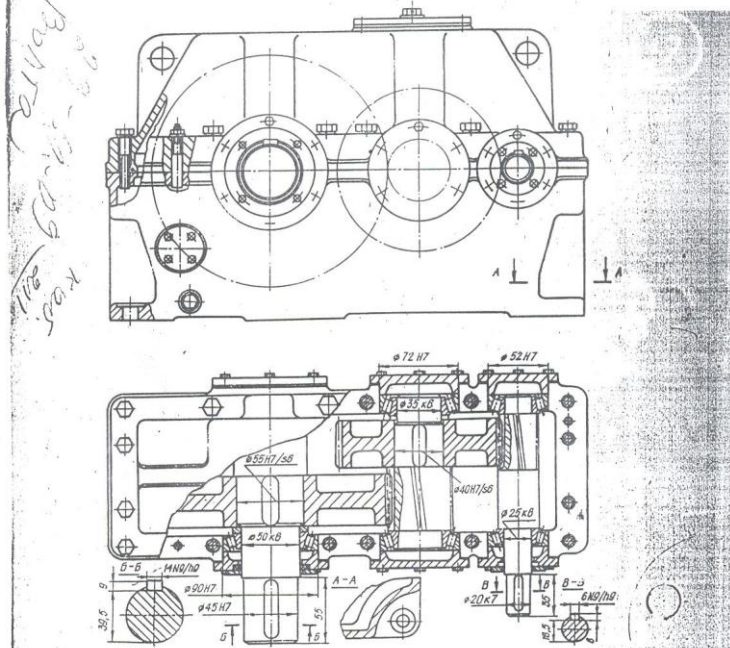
Двухступенчатый цилиндрический редуктор
